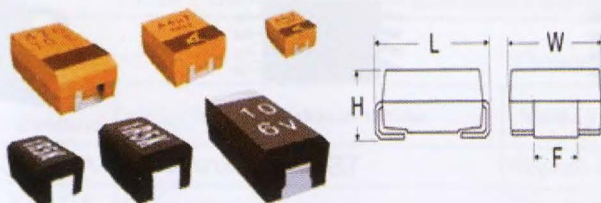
Форма корпусов конденсаторов, резисторов, диодов, стабилитронов в SDM исполнении
